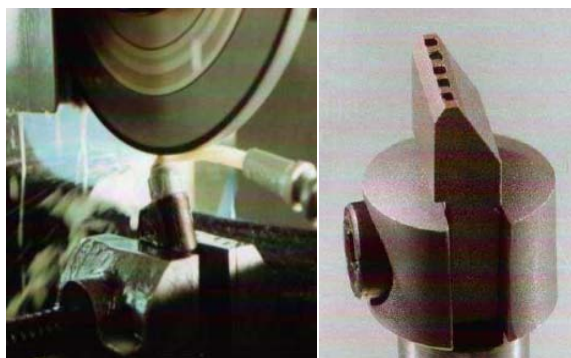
Dressador de ponta simples e pontas múltiplas (Pricken, 1999)
